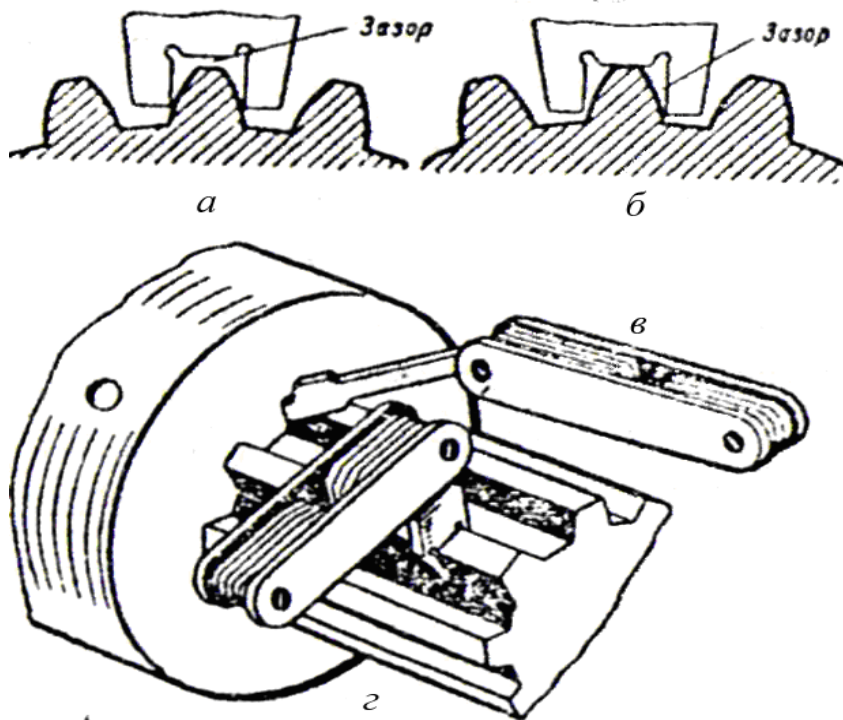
Калибры контроля износа зубьев шестерен:
